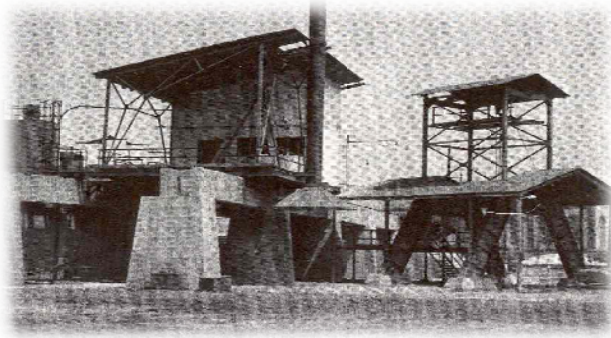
Planta de desulfuración de arrabio desarrollada por el CENIM
